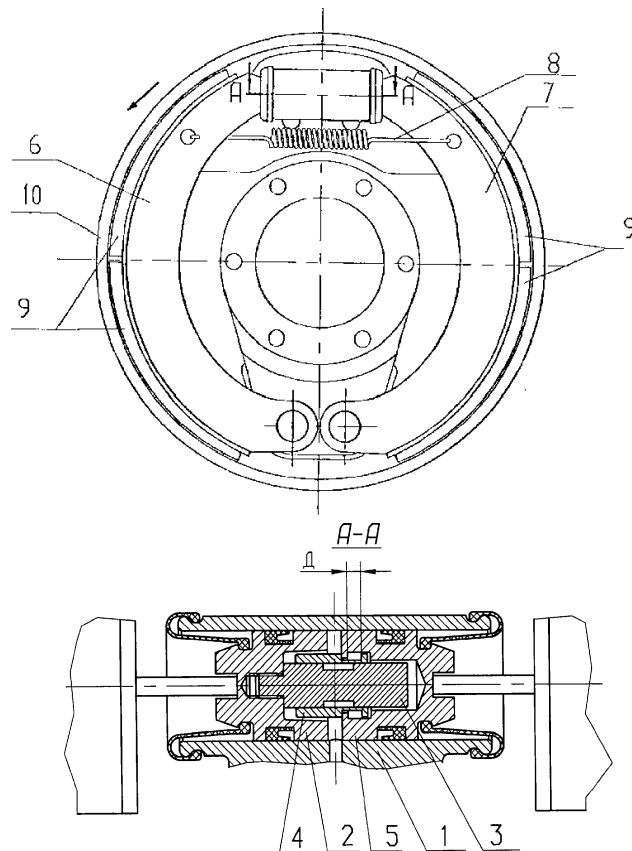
Устройство автоматической регулировки зазора между тормозными накладками и барабаном. Патент России № RU 2223427
